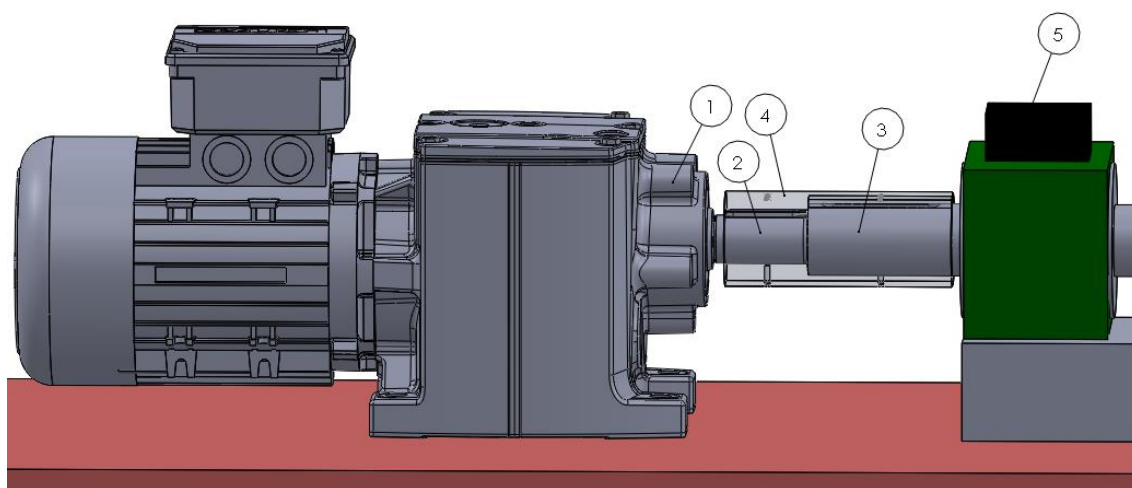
Motor s převodovkou od firmy Lenze [30]
